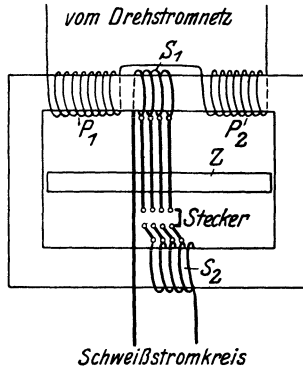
Schweißumspanner mit Streupaketen.
